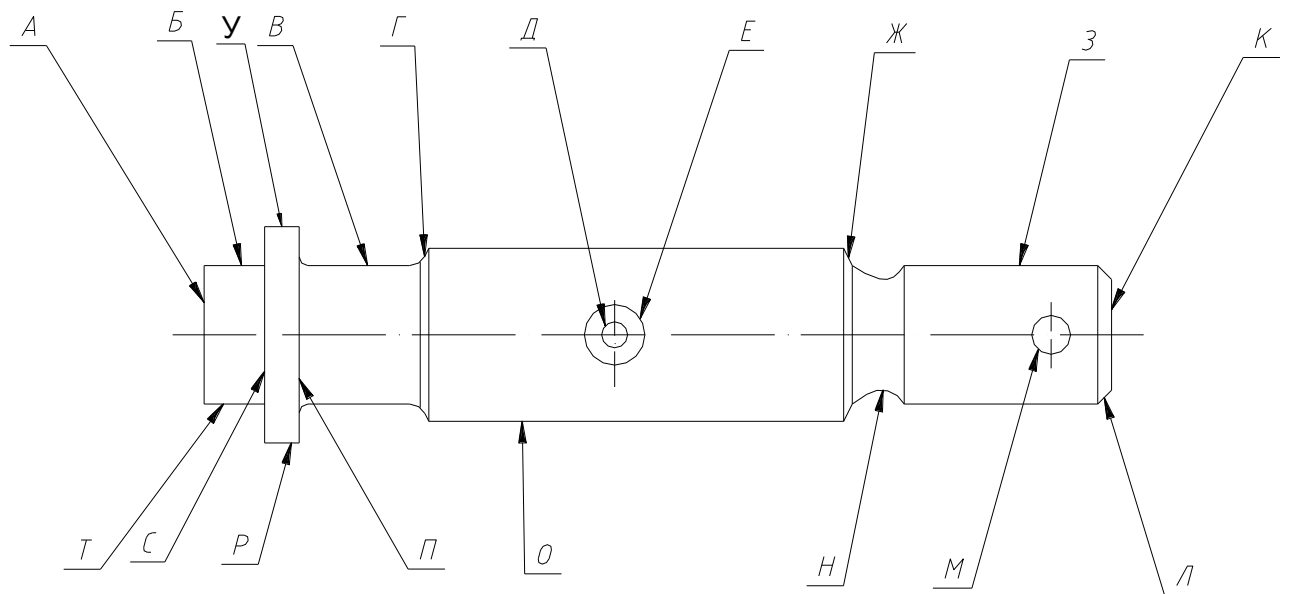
Основні поверхні деталі – палець ПП-16.644
